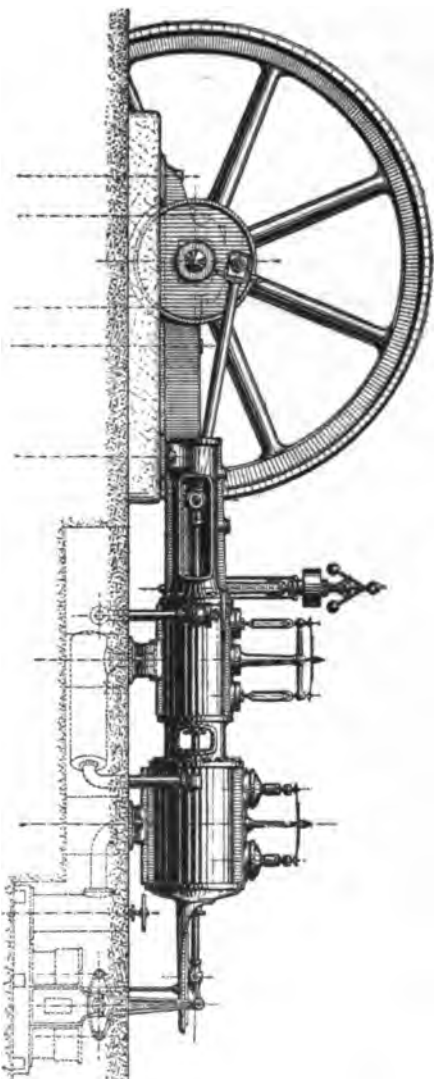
Tander-Maschine mit Solmann-Steuerung.
